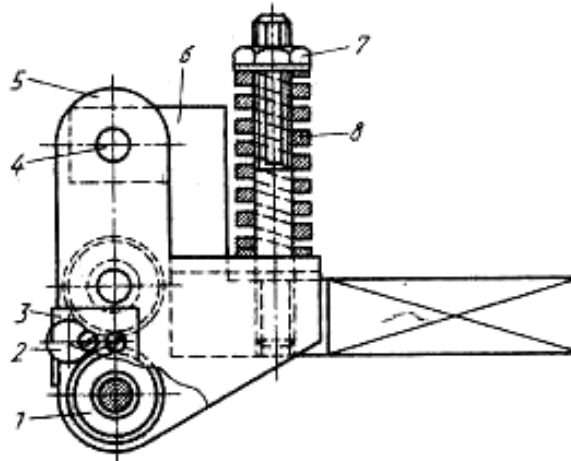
Оправка важільної для вигладжування поверхонь деталей підвищеної твердості [30]
